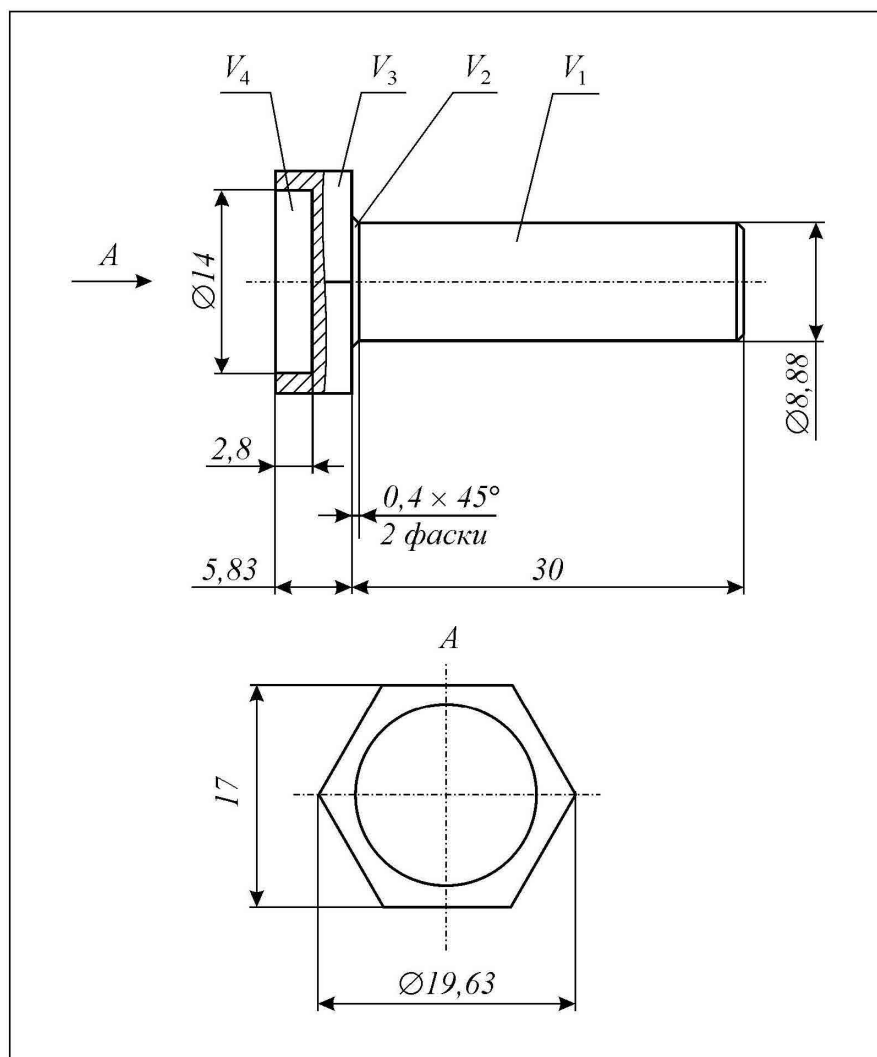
Кресленик деталі «Болт М10×30»
